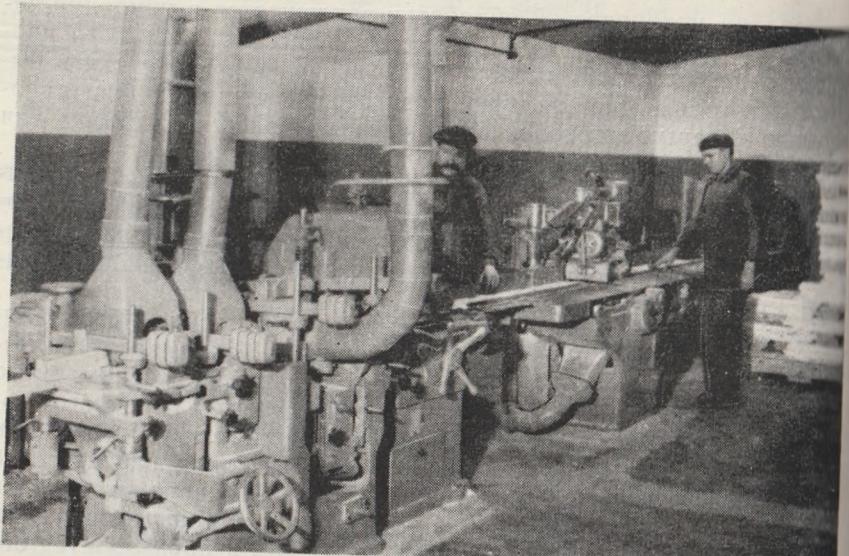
Поточная полуавтоматическая линия по обработке брусковых деталей
